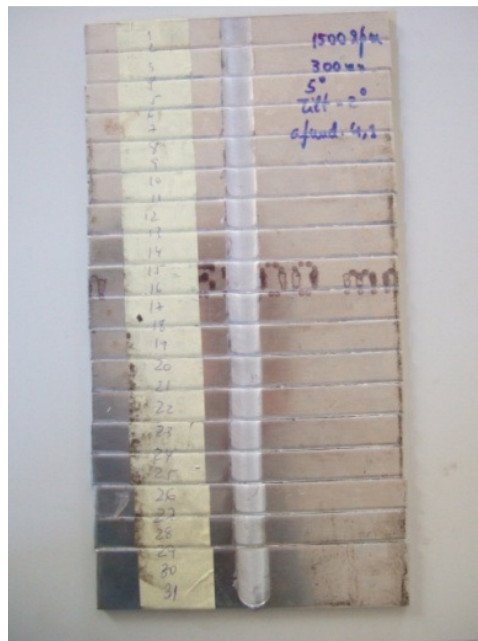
Chapa com a soldadura 6 já cortada pela guilhotina
